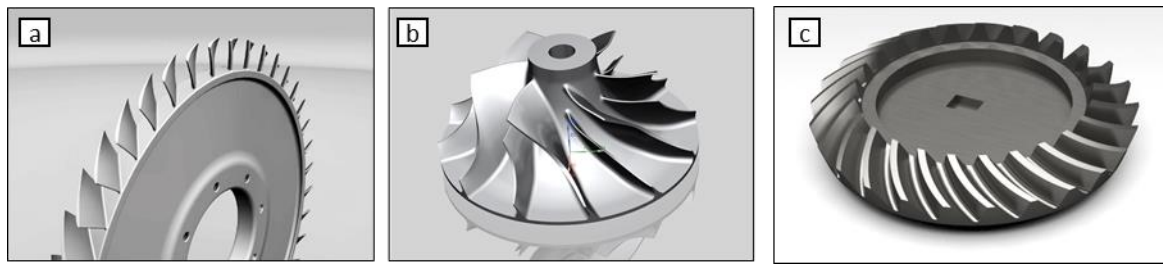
Componentes de geometría compleja: a) Blisk, b) Impeller y c) Engranaje.
